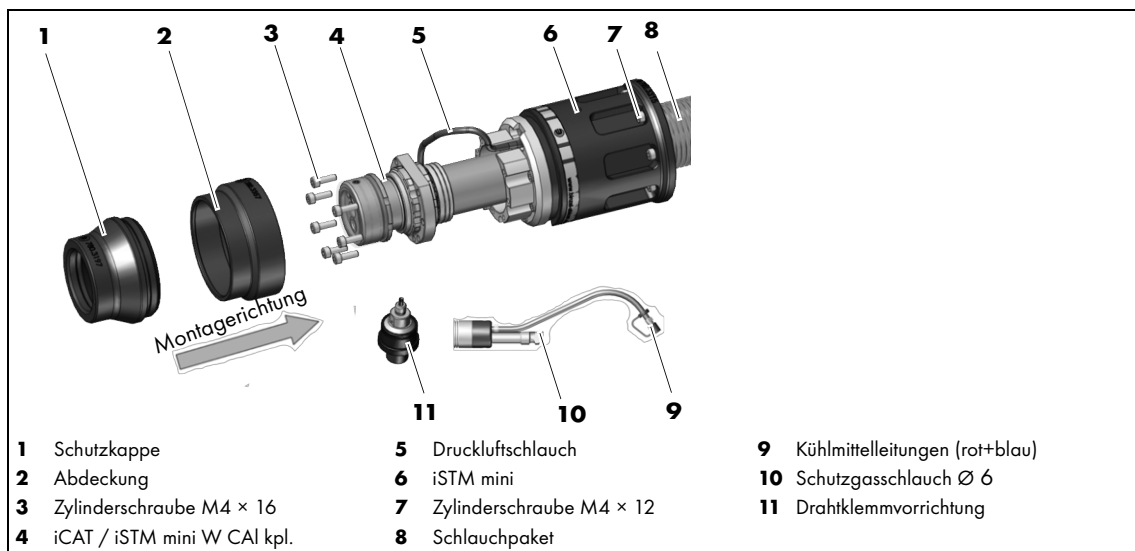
Schlauchpaket montieren iSTM mini für ABIROB® W mit Wire-Brake
